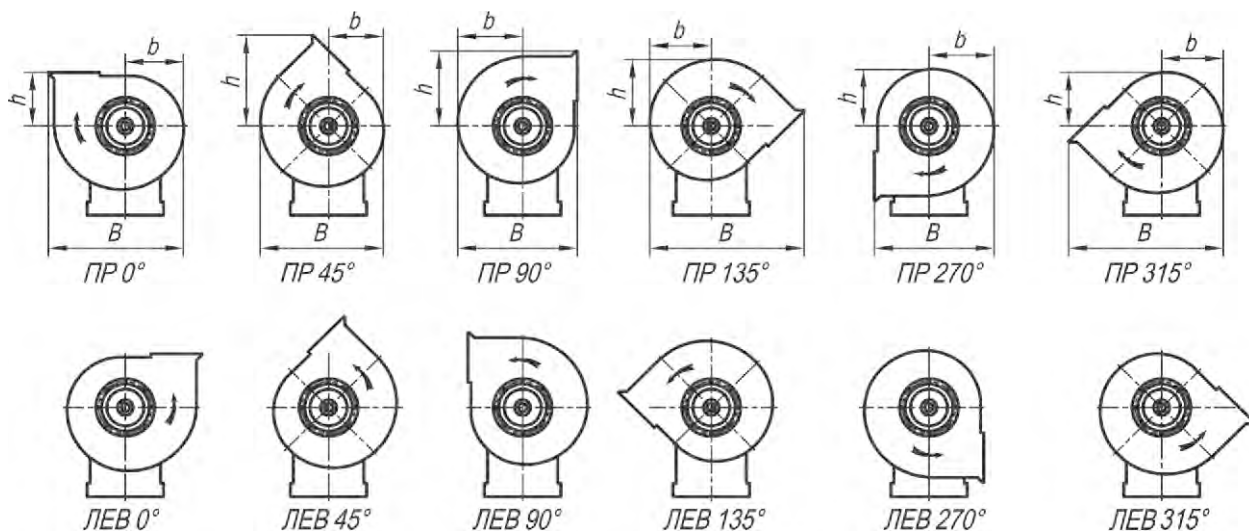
Положение корпуса вентилятора ВР 132-30 исп-1.
